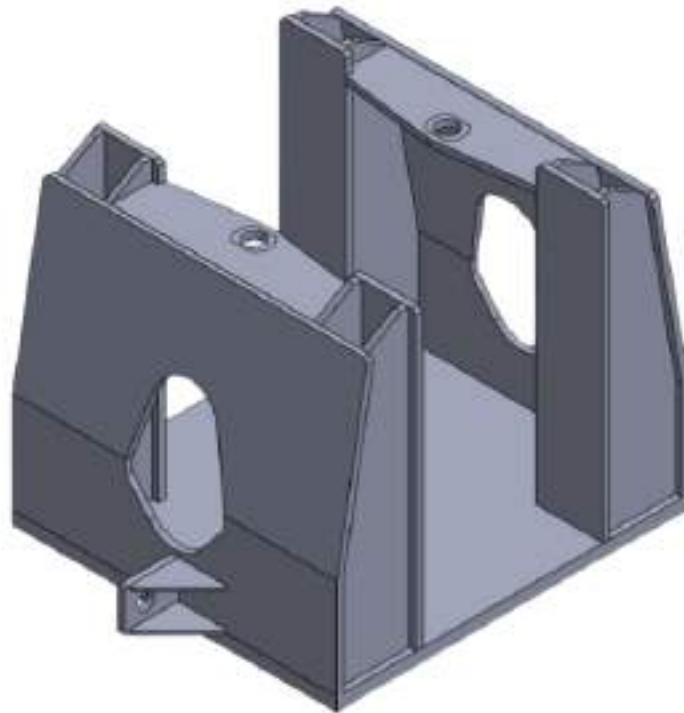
Vista isométrica del carro Y sin componentes ni accesorios.
